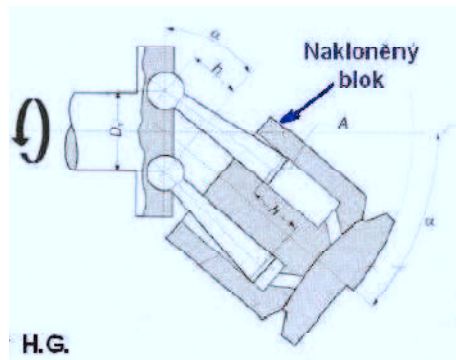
Axiální pístové čerpadlo s nakloněnou deskou [2]
